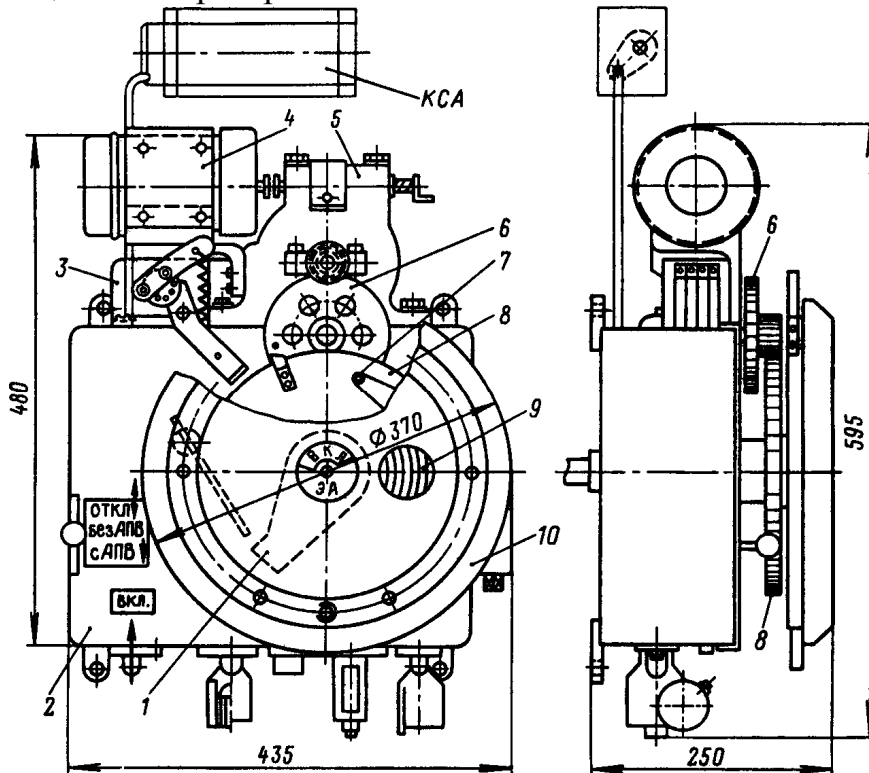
Пружинний привод з моторним редуктором ППМ-10:
